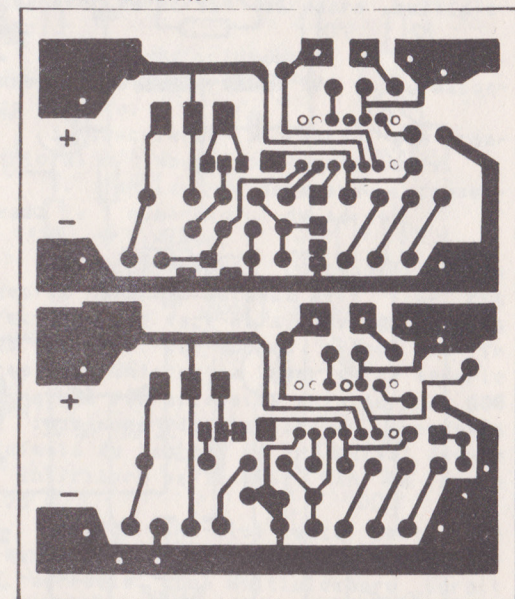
Cablajul imprimat (vedere dinspre partea placată)
